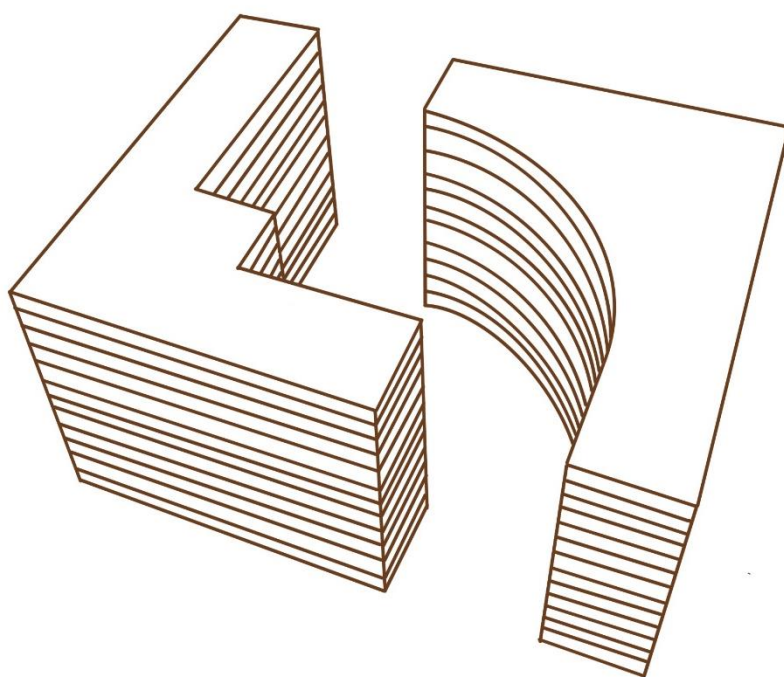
Dessin : Axonométrie du moule en bois composé de plaques récupérées et superposées.
